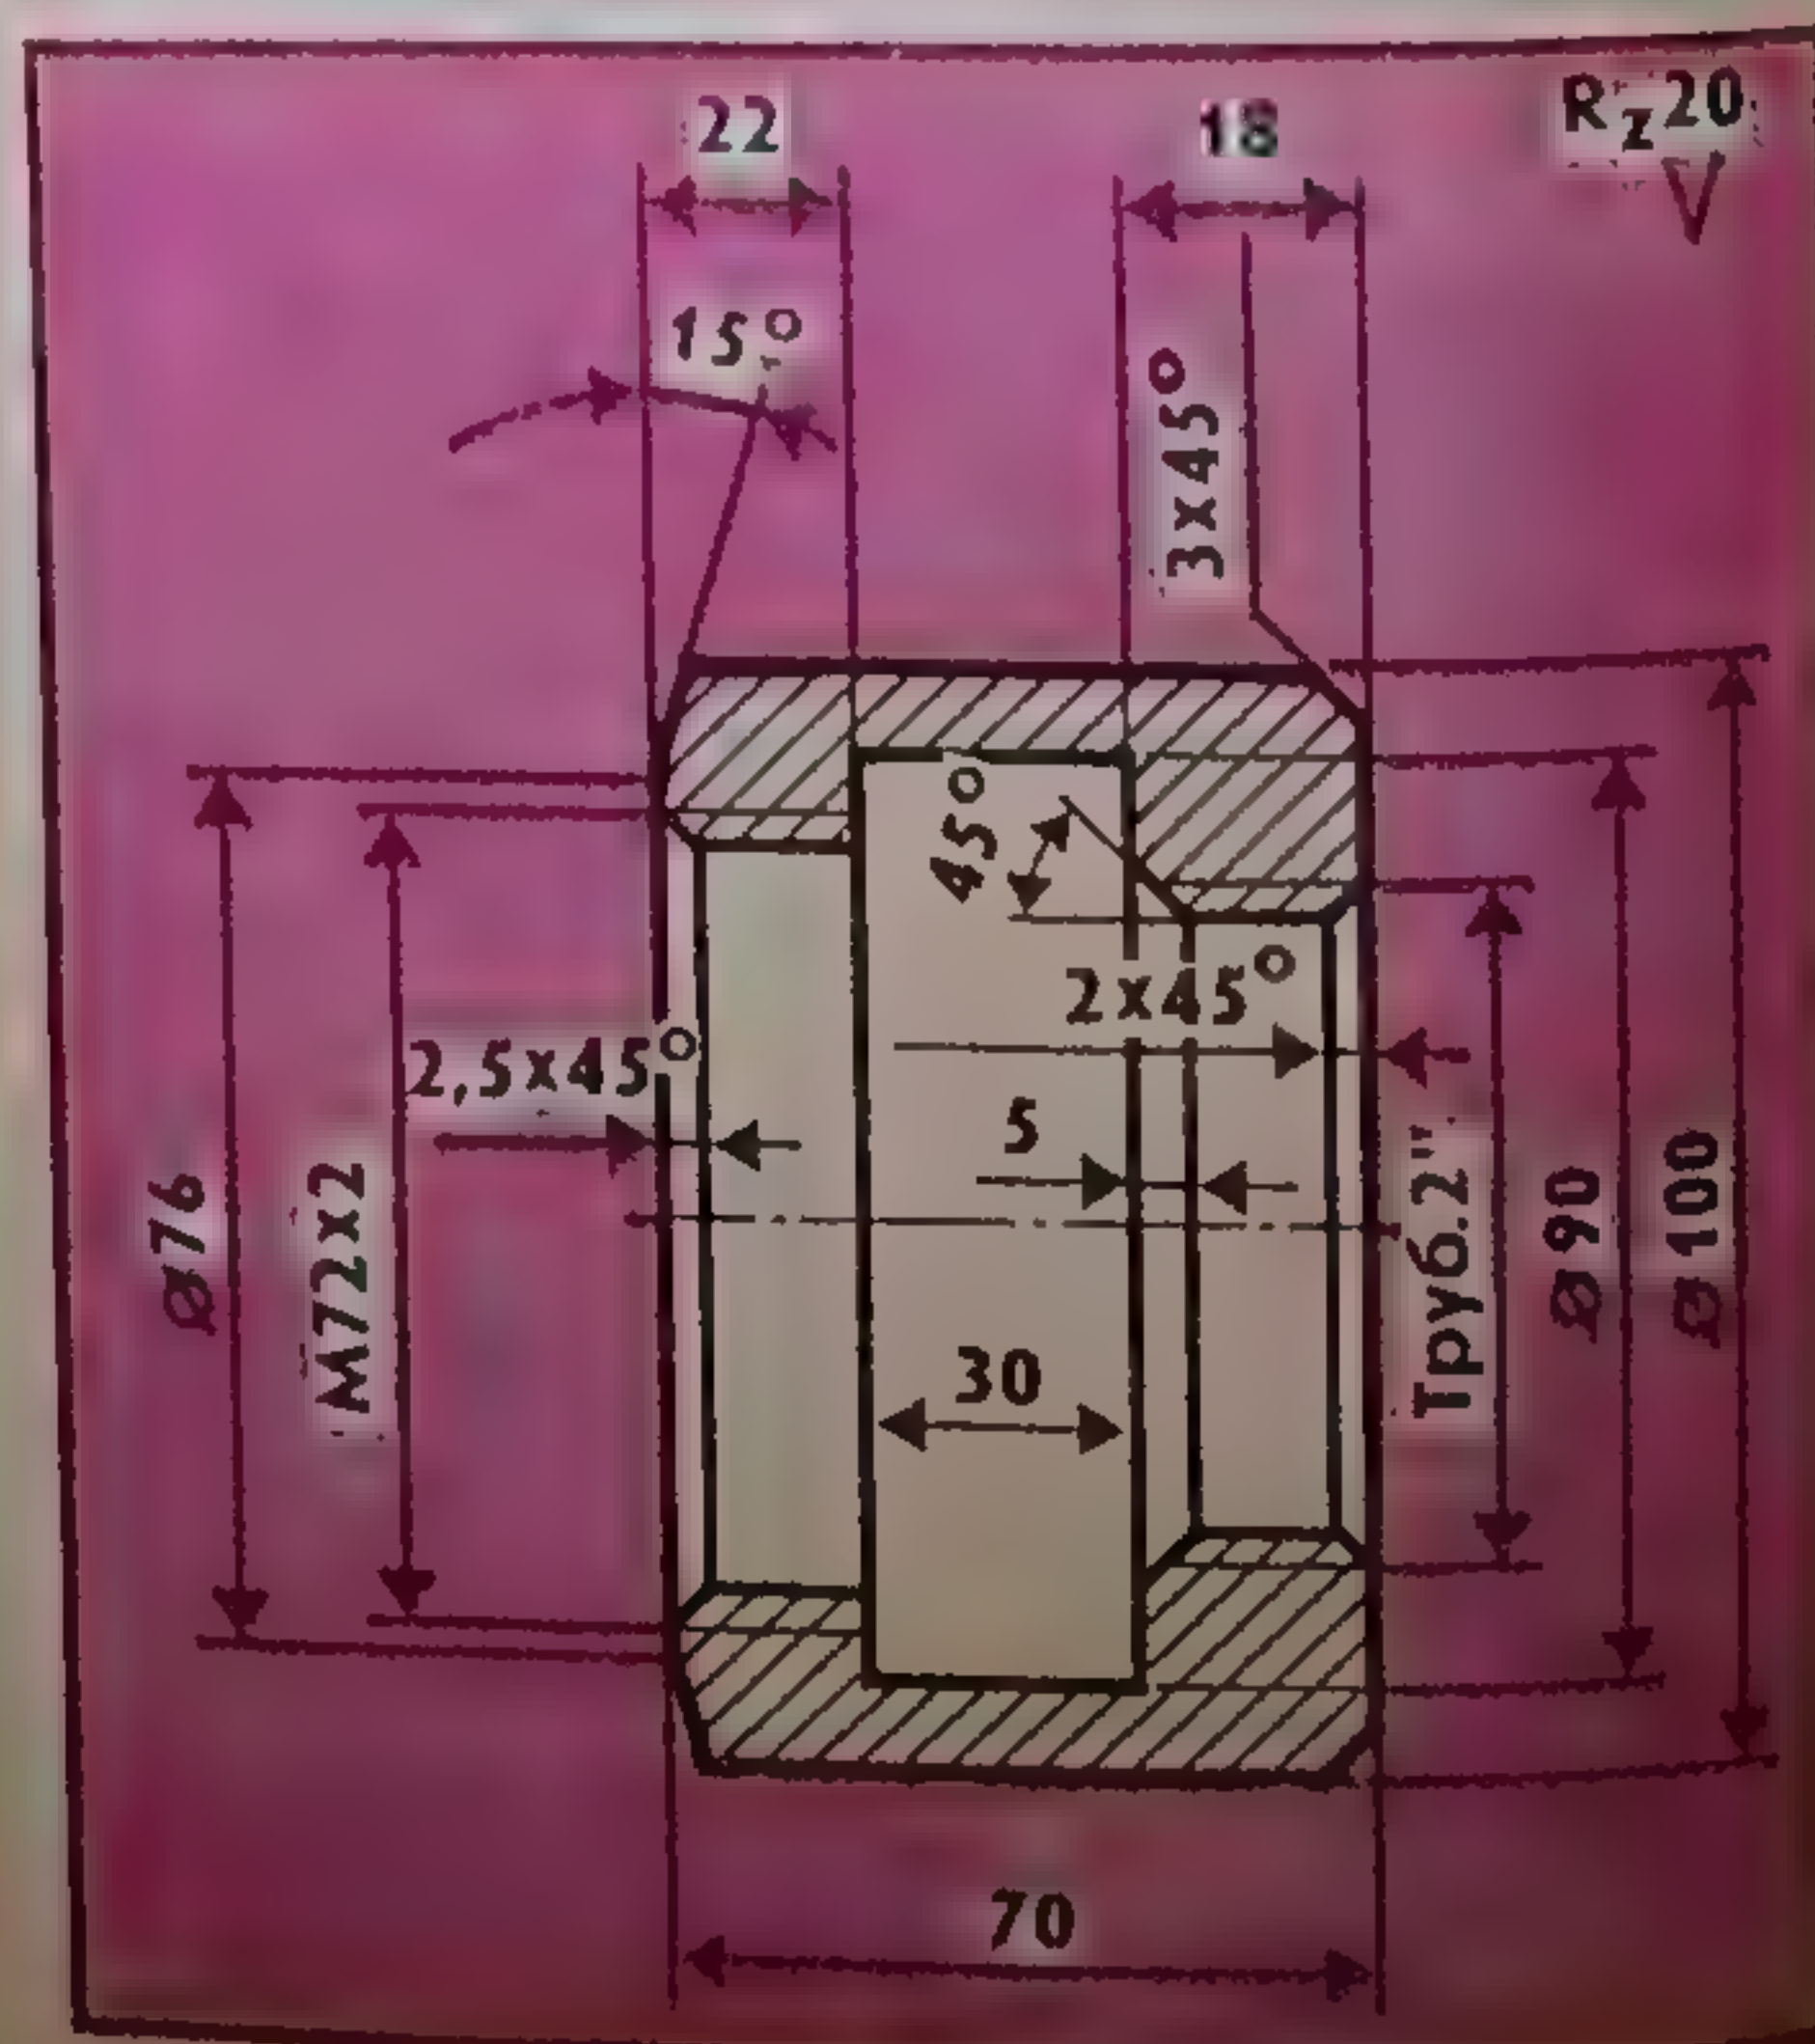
Соединительные муфты: № 1 — для буровых штанг; № 2 — для фильтра
